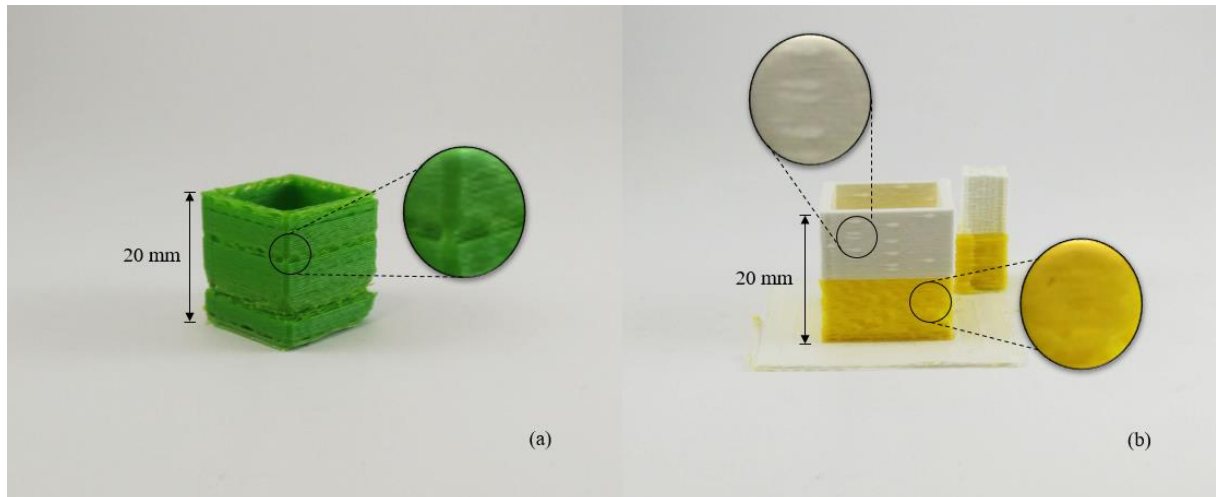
Fenómenos de impressão Delta de (a) sob extrusão (b) sobre extrusão.
